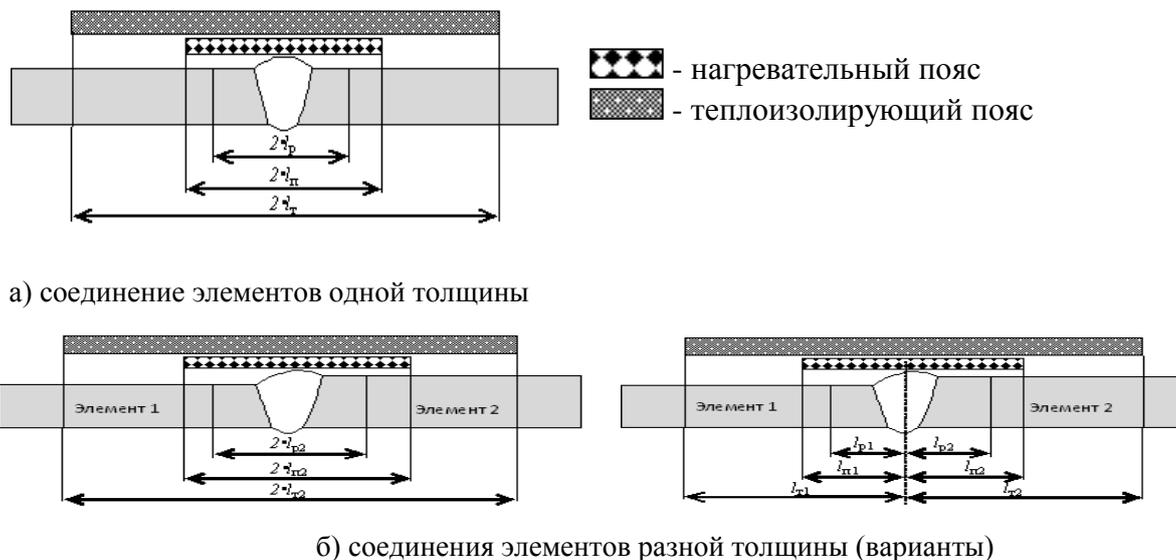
Зоны нагрева при термической обработке стыковых сварных соединений
